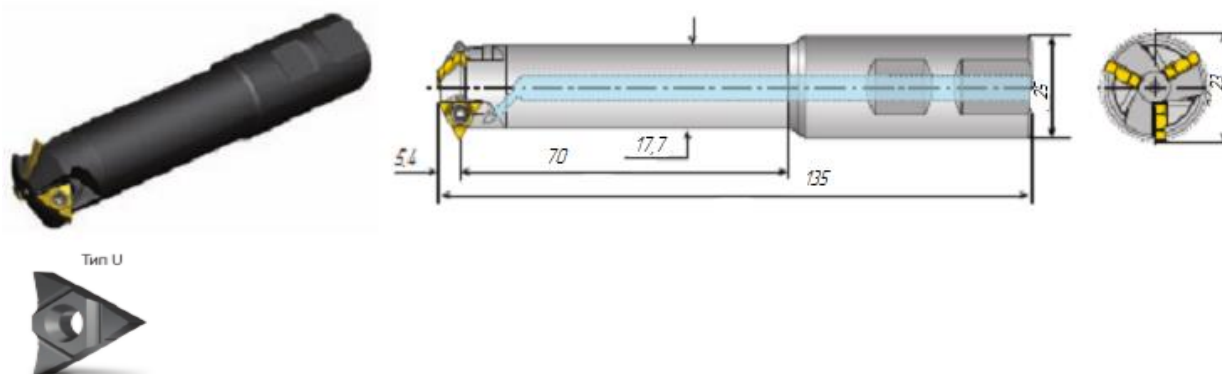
Фреза со сменными пластинами, с каналом для подачи СОЖ и сменная пластина.
